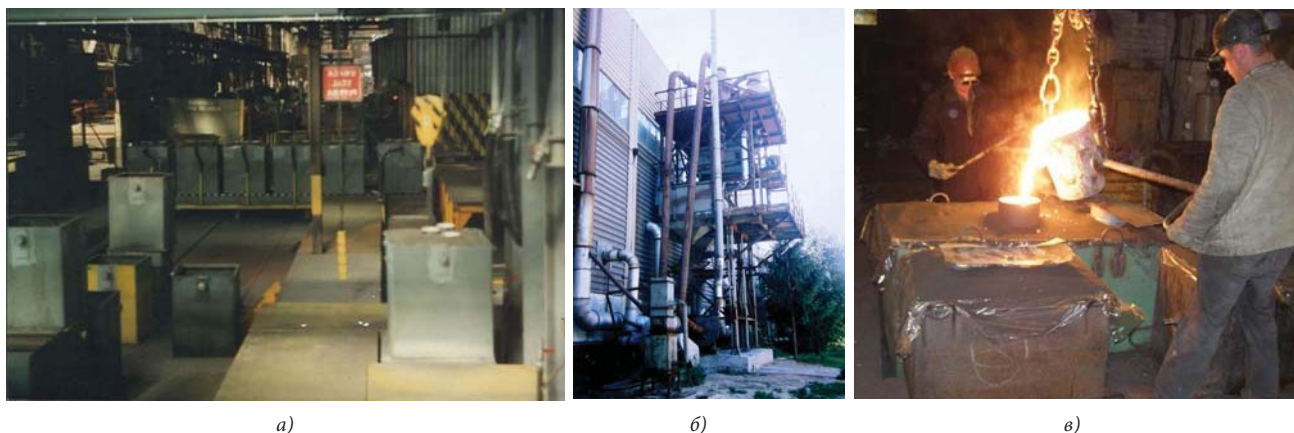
Фото участков: а) формовочно-заливочного, б) подготовки песка, в) операции заливки форм.
